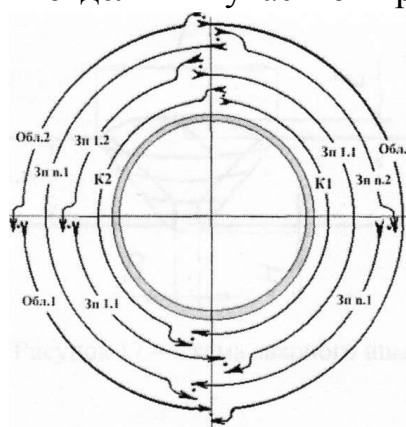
Схема сварки и последовательность сварки отдельных участков шва
